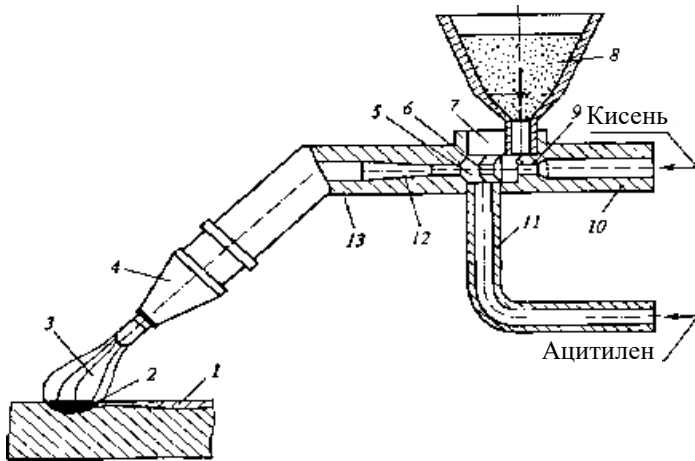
Установа, обладнана зварювальним пальником: 1 – наплавлена поверхня; 2 – зварювальна ванна; 3 – полум'я; 4 – мундштук; 5 – камера змішування; 6, 9 – інжектори; 7 – змішувальна камера; 8 – порошок; 10 – киснева трубка; 11 – ацетиленова трубка; 12 – канал; 13 – трубка
